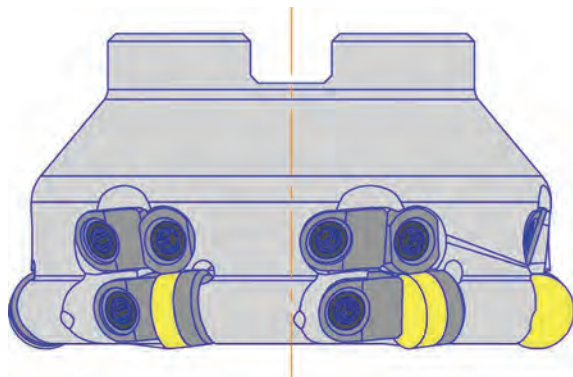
Торцевая фреза для крепления клином пластины без отверстия
